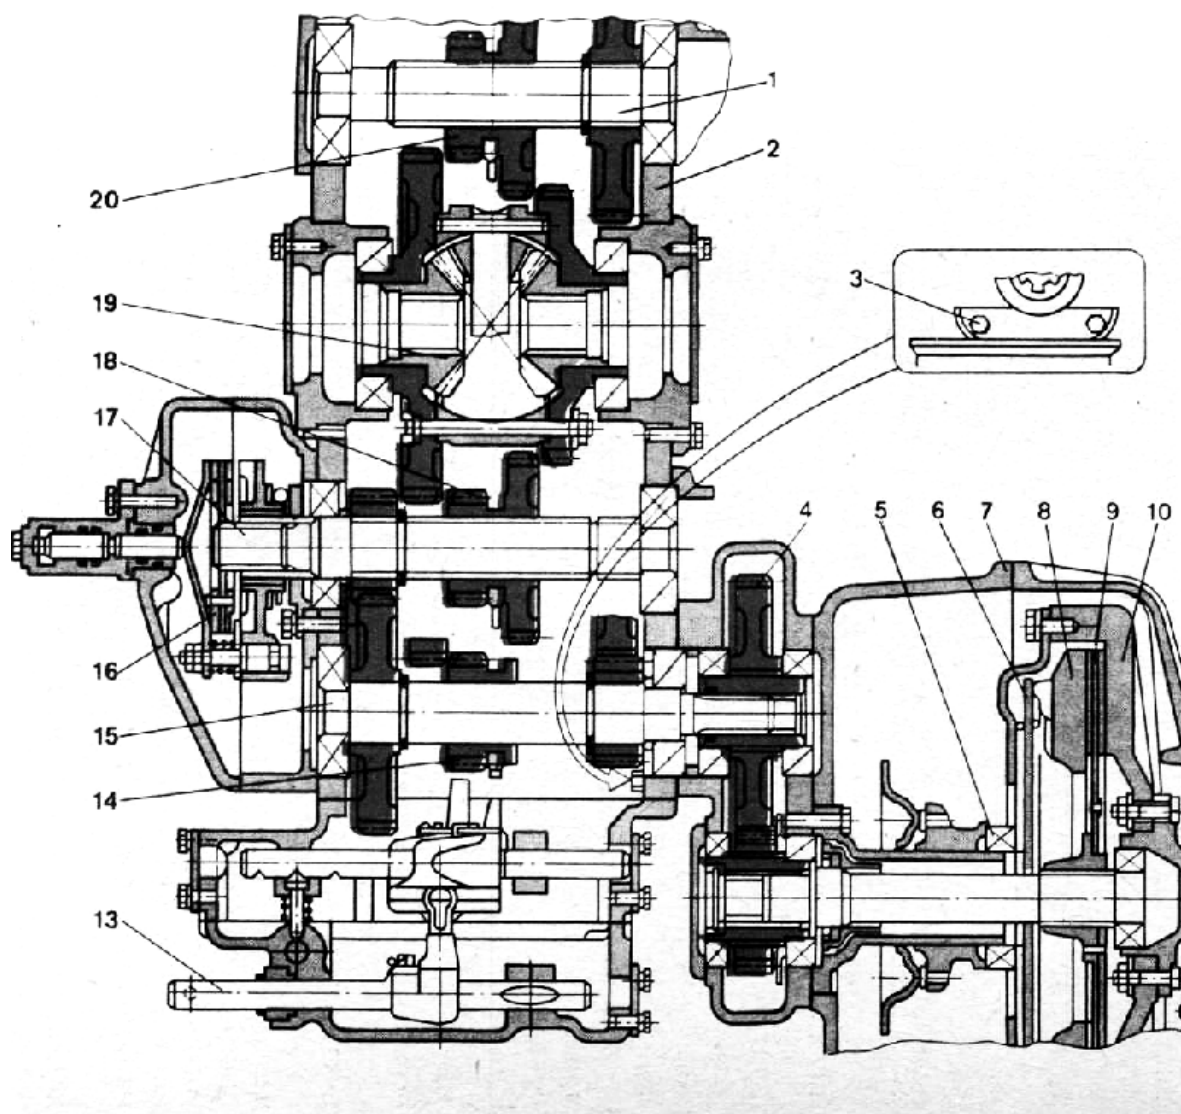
Коробка диапазонов скоростей и сцепление (разрез):
